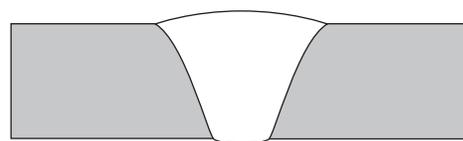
Поперечное сечение контрольного сварного шва
